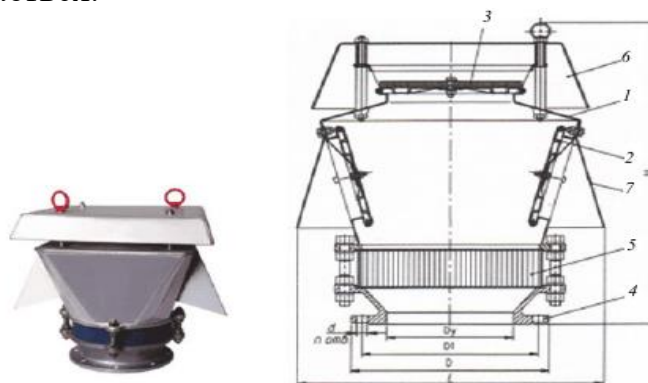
Клапан КДМ-200: 1 - корпус; 2 - тарілка вакууму; 3 - клапан тиску; 4 - приєднувальний фланець; 5 - вогневий запобіжник; 6 - кришка; 7 – козирок
